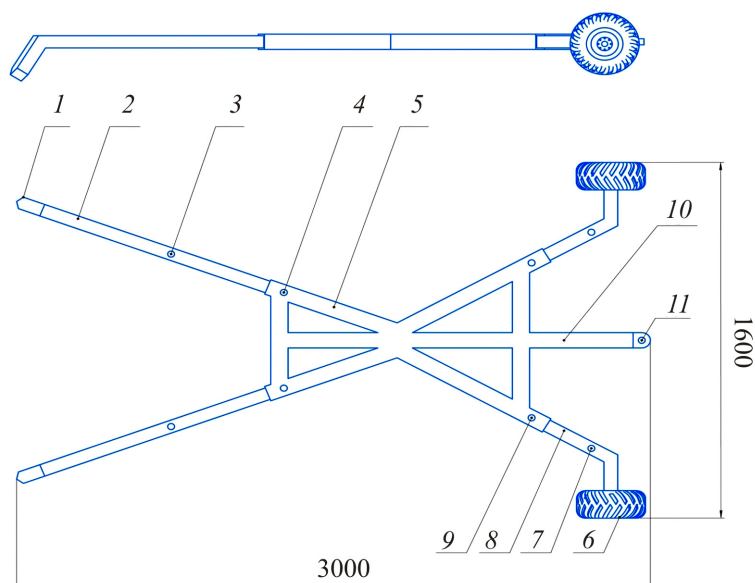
X-образная схема несущей платформы мини-экскаватора: 1 – наконечник опоры; 2 – выносная опора; 3, 4 – отверстия для фиксации опоры; 5 – рама; 6 – колесо; 7, 9 – отверстия для фиксации колес; 8 – колесная балка; 10 – выноска для фаркопа; 11 – фаркоп
